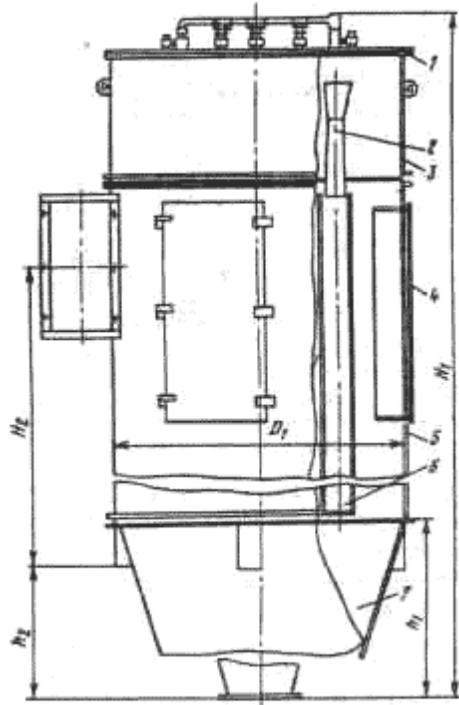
Схема очистки воздуха от системы вентиляции.
